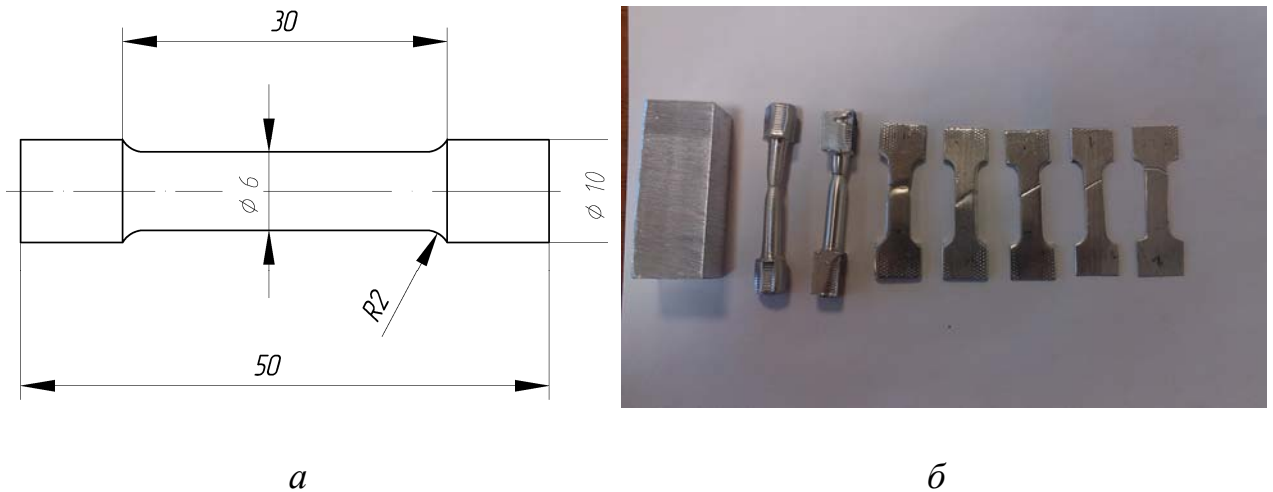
Размеры (а) и вид (б) образцов для испытания механических свойств
